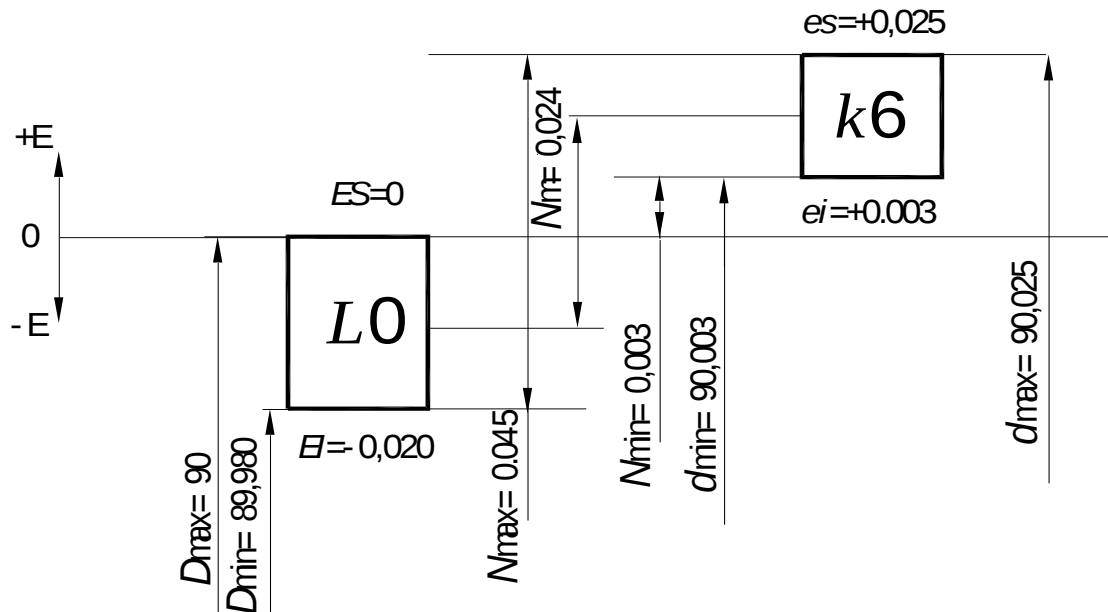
Схема расположения полей допусков внутреннего кольца подшипника и вала
